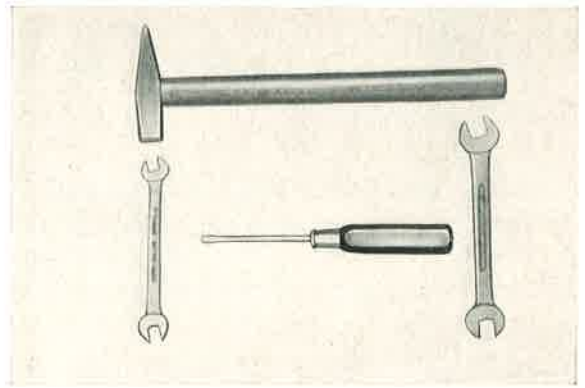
Zusammenstellung der Werkzeuge, wie sie für die Arbeit Gruppe LAZ, (1-5) gebraucht werden.
